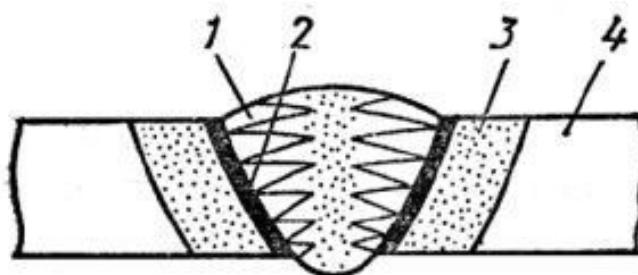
Сварное соединение: 1 – сварной шов; 2 – зона сплавления; 3 – зона термического влияния; 4 – основной металл.
